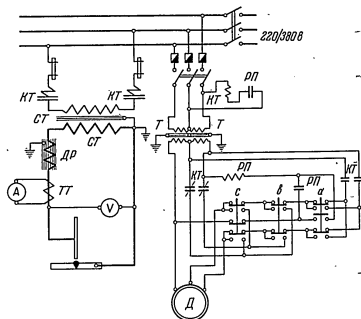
Принципиальная электрическая схема сварочного трактора ТС-17-М для сварки на переменном токе:
